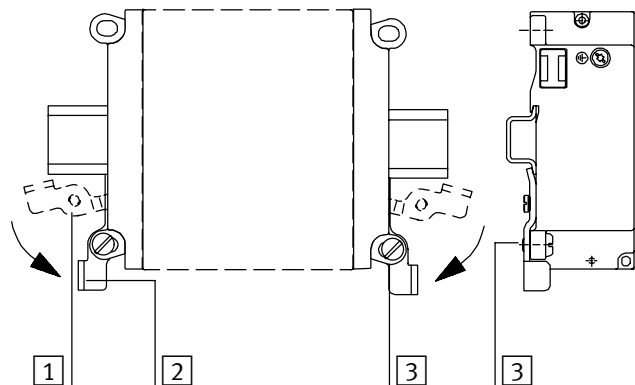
/3: Montage sur rail d'un terminal de distributeurs type 03
